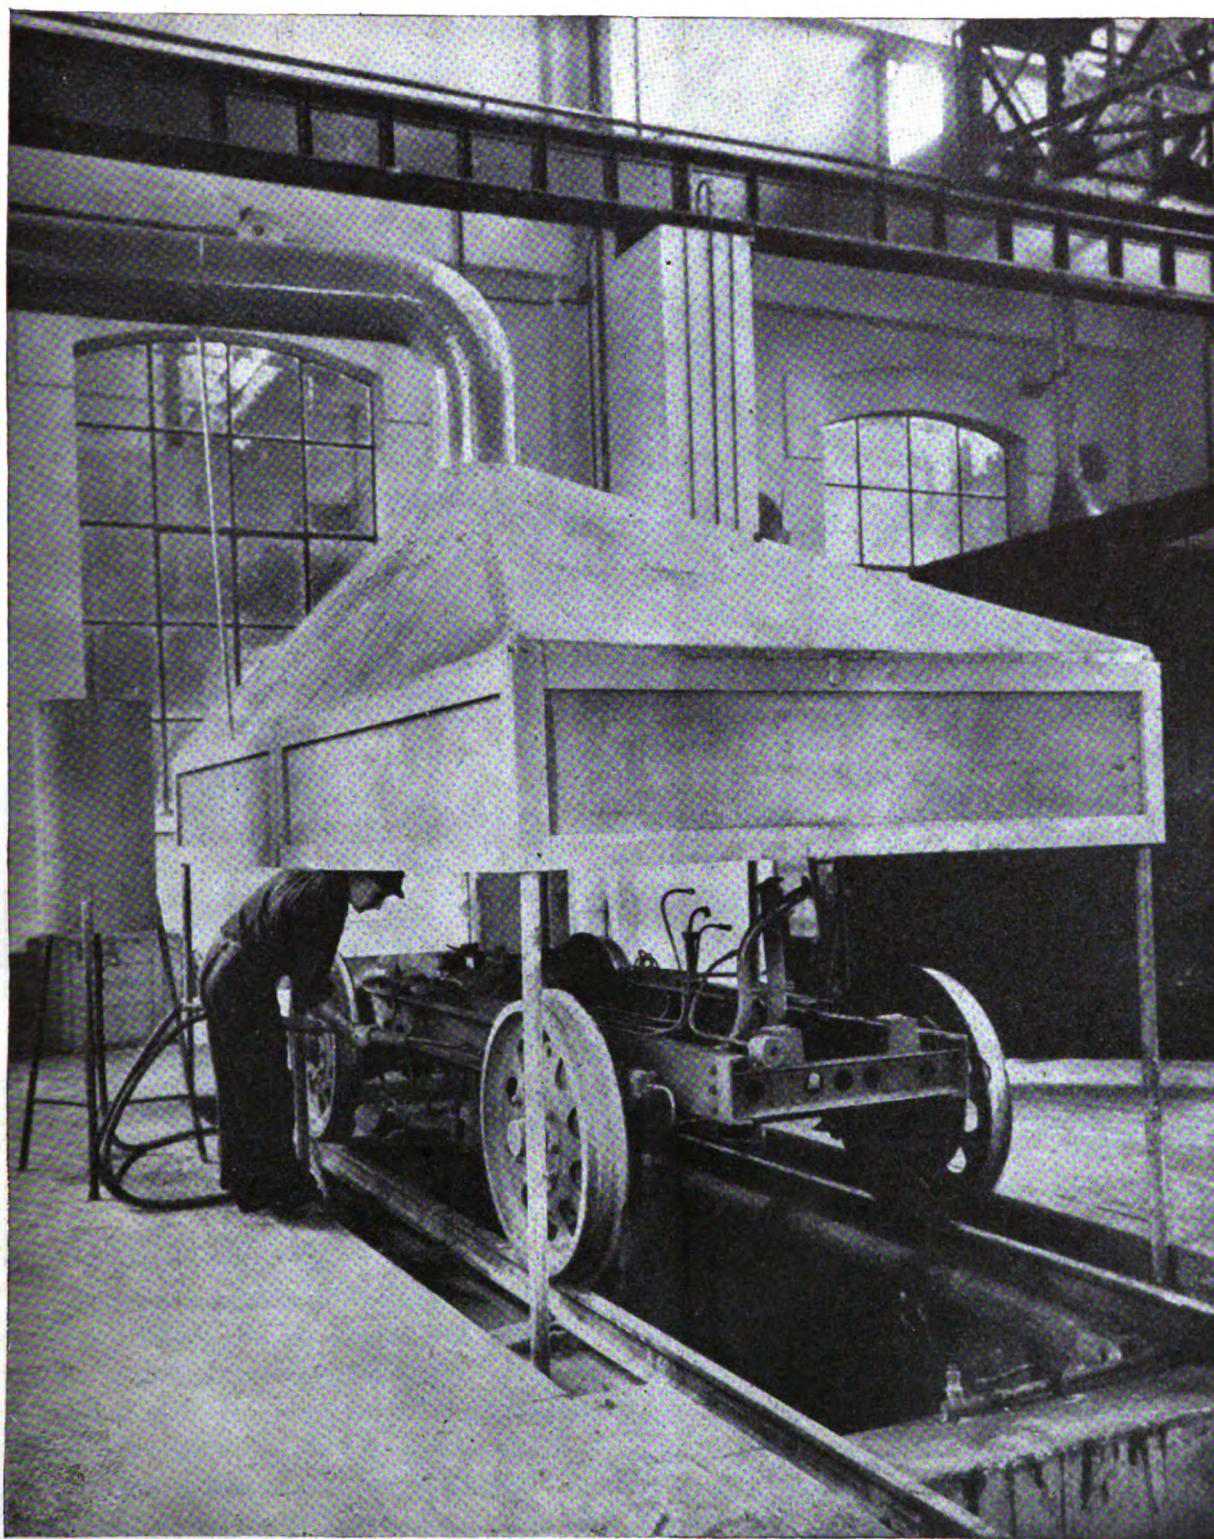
Cappa per il lavaggio dei carrelli in corso di smontaggio.
